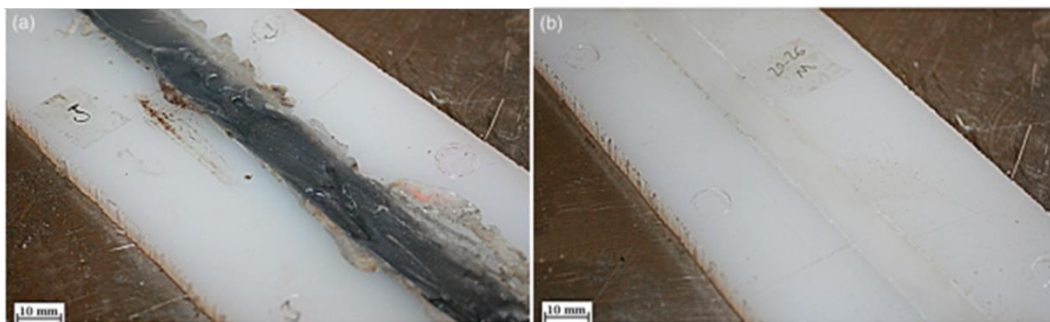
Amostras de PA6 soldadas: a) Parâmetros incorretos, b) Parâmetros ideais, [28].
